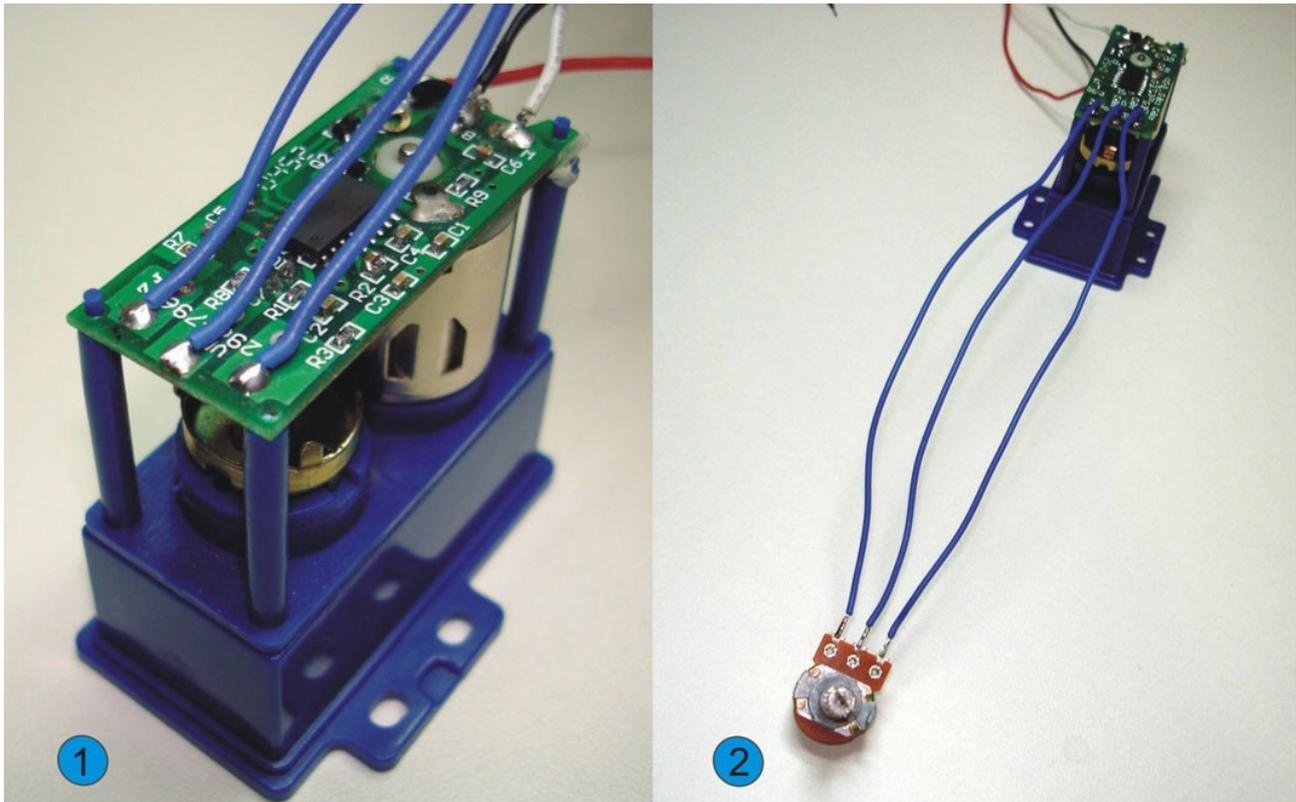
Servo-motor com potenciômetro para controle da rotação. 1-Fios soldados na placa de controle. 2-Placa adaptada com o potenciômetro
